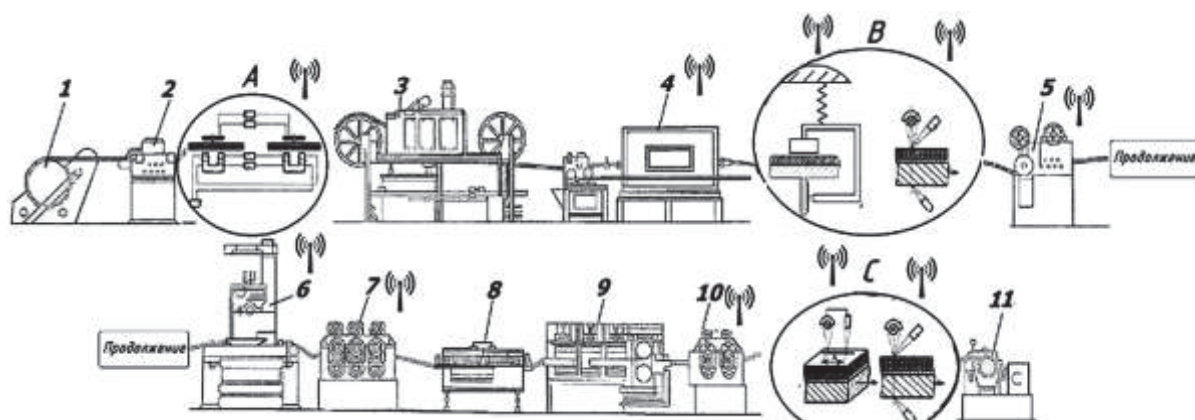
Линия производства четырехслойного металлофторопластового ленточного материала
